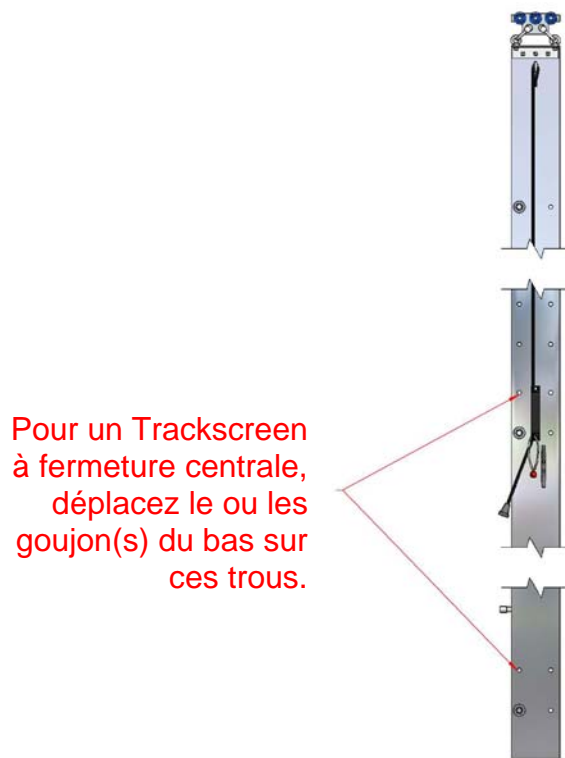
, Poteau pour un Trackscreen double, fermeture centrale
